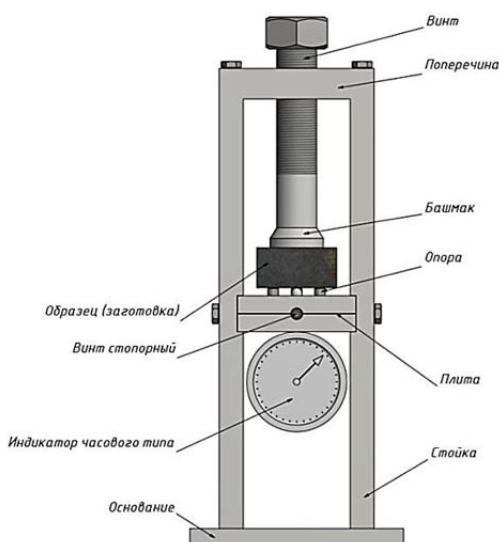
Установка для определения погрешности закрепления заготовок
